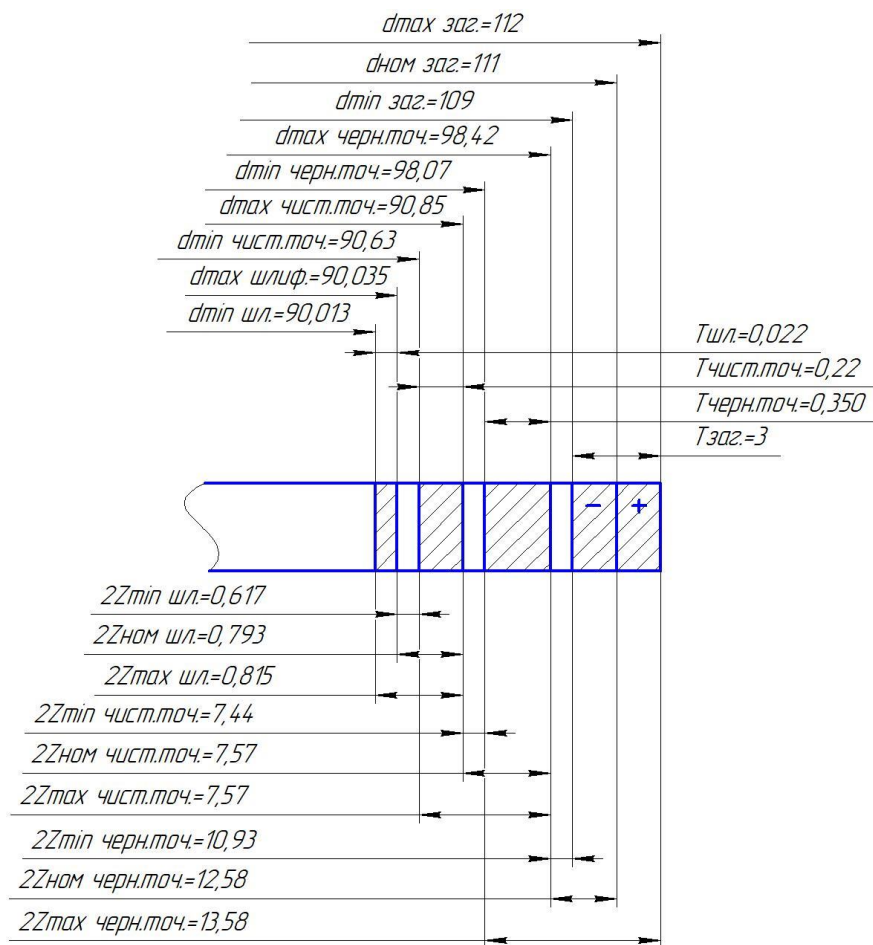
Схема розташування припусків і допусків при обробки поверхні Ø90m6 (+0,035; +0,013)
